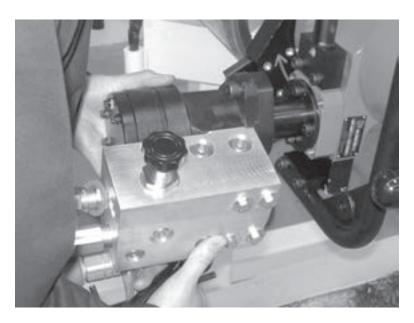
Le moteur hydraulique est interchangeable avec le moteur pneumatique.
